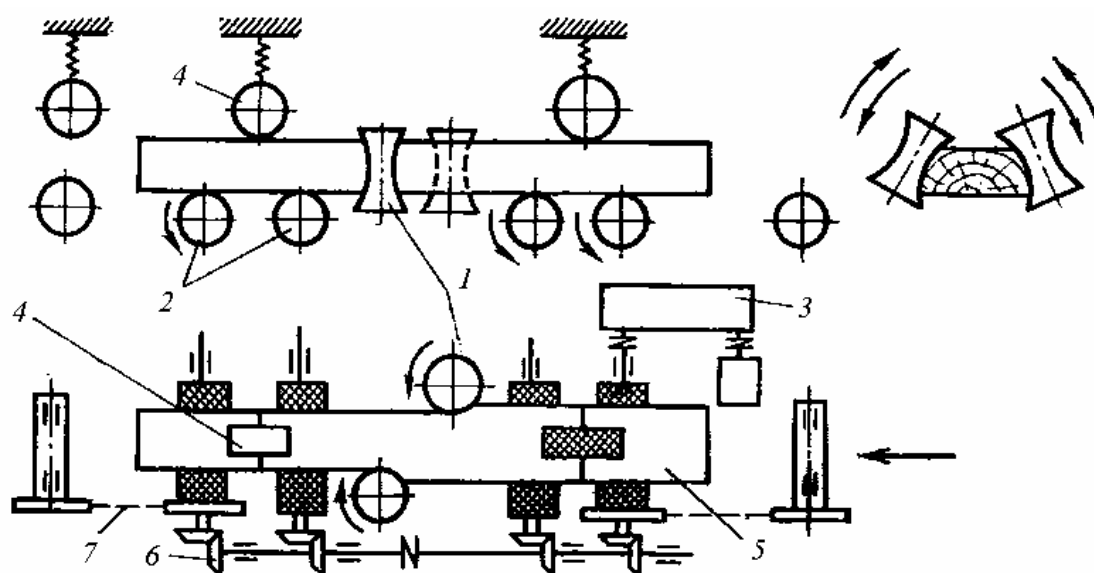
Схема шпалооправочного станка ЛО-48: 1 – барабанная ножевая головка; 2 – приводные вальцы; 3 – привод вальцов; 4 – прижимные вальцы; 5 – шпала; 6, 7 – коническая и цепная передачи
